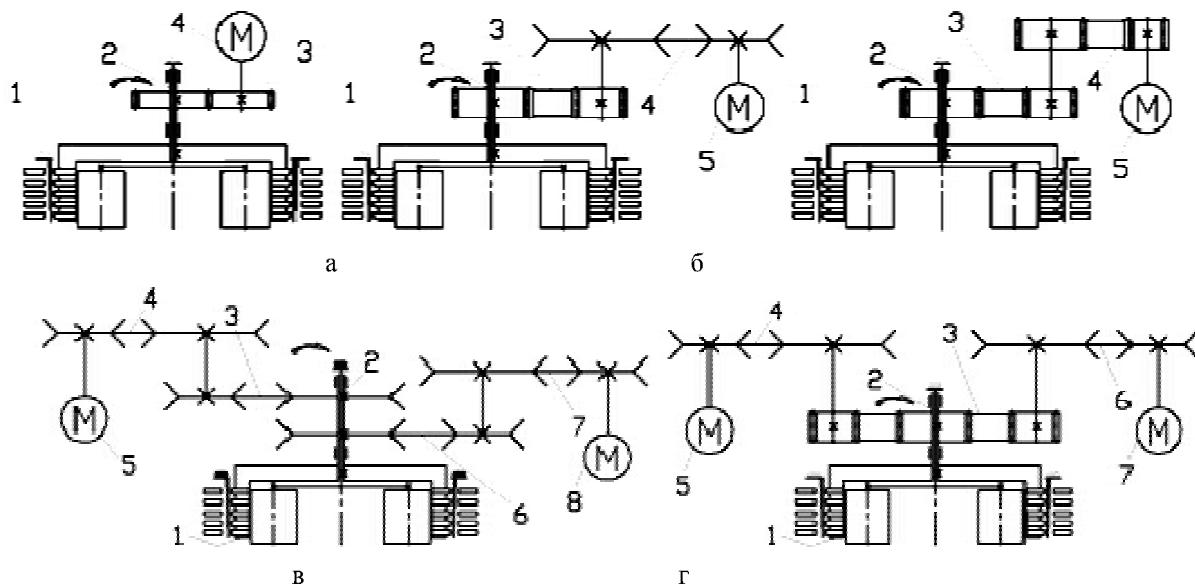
Схемы приводов прессов с кольцевой матрицей
